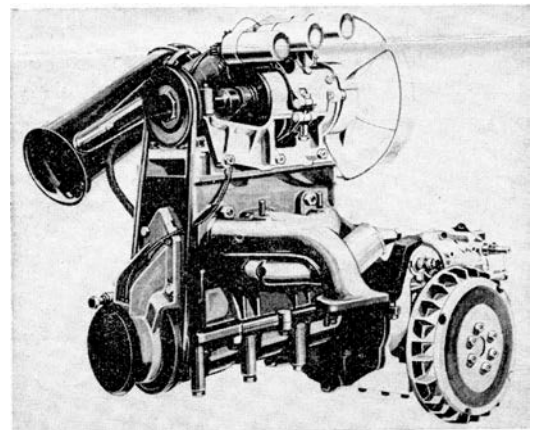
Двухтактный 3-цилиндровый двигатель DKW-Юниор
